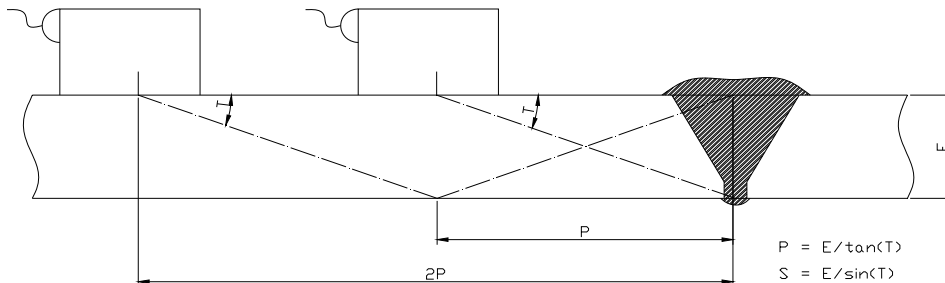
Esquema de distancias de inspección de soldadura
